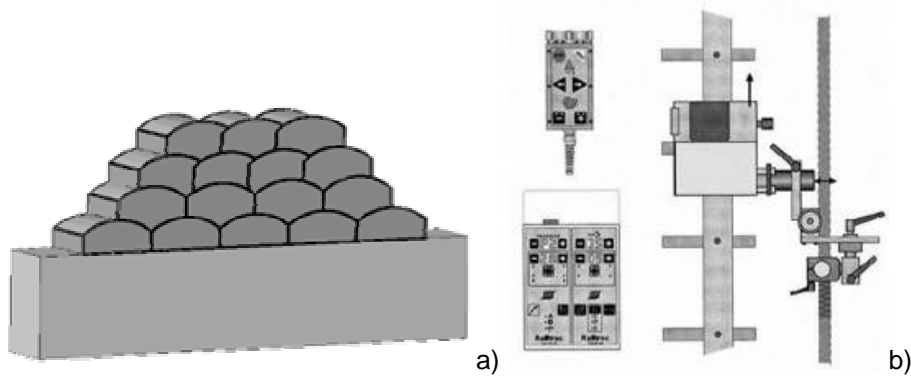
a). Secuencia de soldadura, b) Equipo Railtrac FW1000
